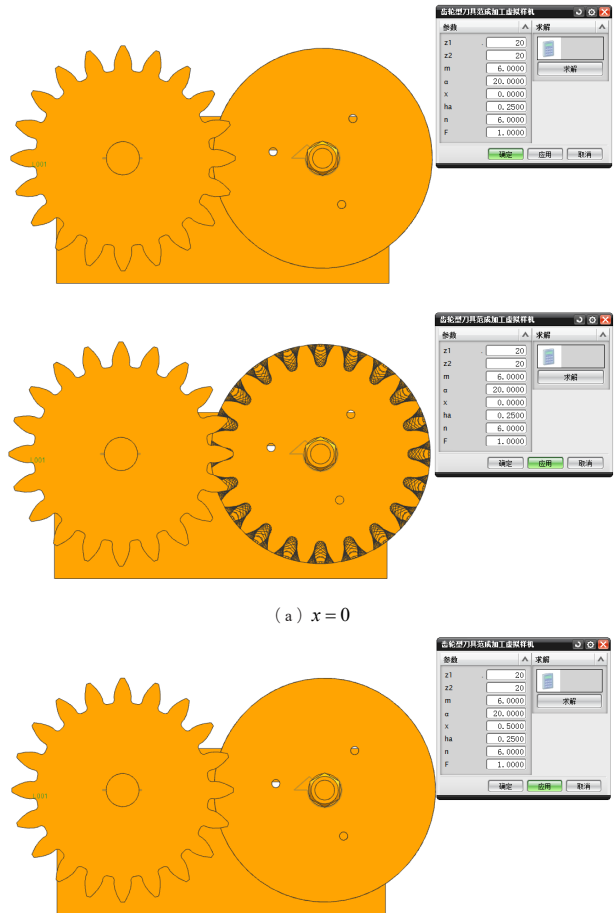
齿轮型刀具范成加工数字化虚拟仿真实验平台
